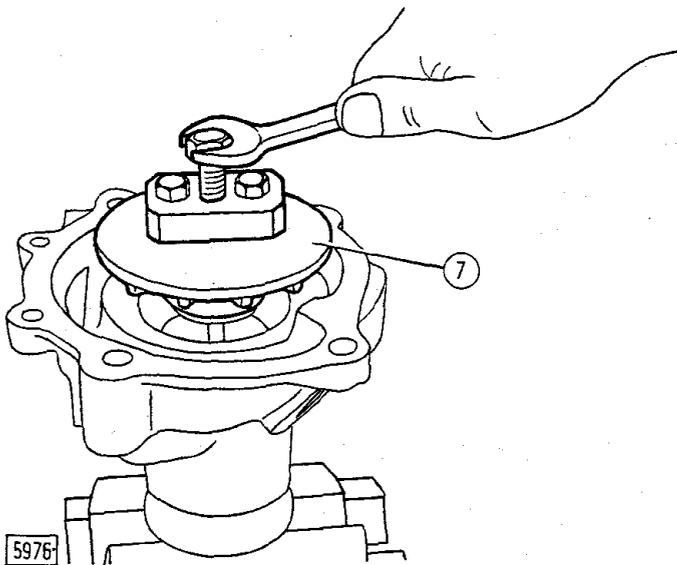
Smontaggio della girante (7) mediante l'estrattore 291182/1.
